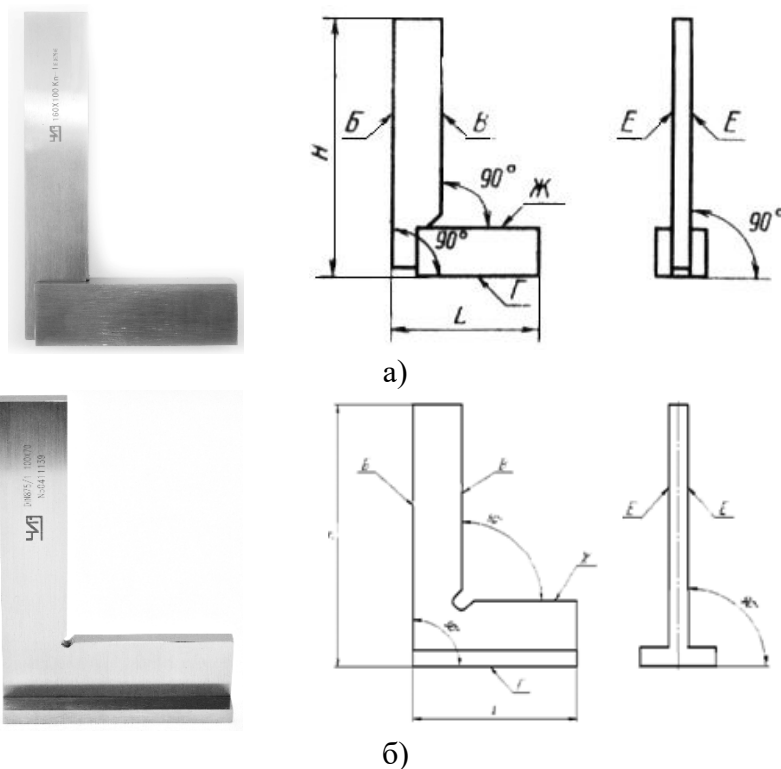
Общий вид угольников УП, обозначение основных размеров и поверхностей
